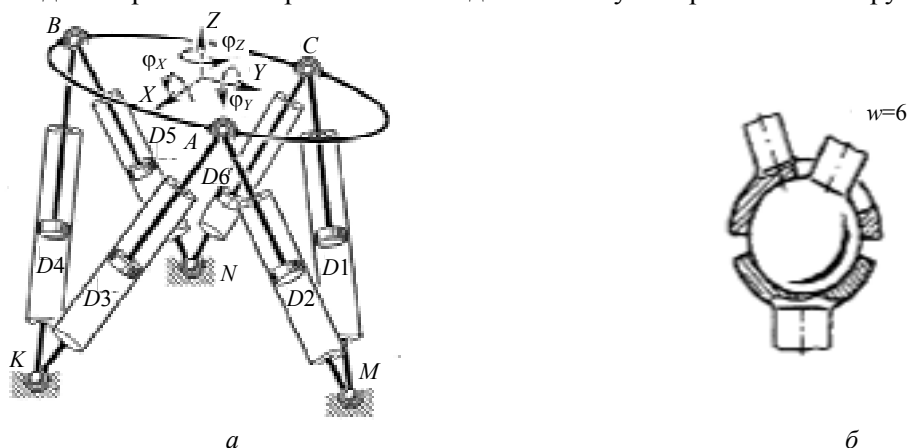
Механизм станка с параллельной кинематикой на основе Платформы Стюарта: структурная схема (а), сдвоенный сферический шарнир (б)
